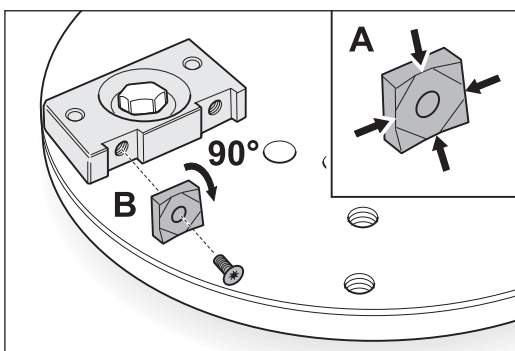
Eine Wendeschneidplatte hat vier Schneiden (A). Nach Verschleiß oder Beschädigung einer Schneide die Wendeschneidplatte um 90 Grad drehen (B).
